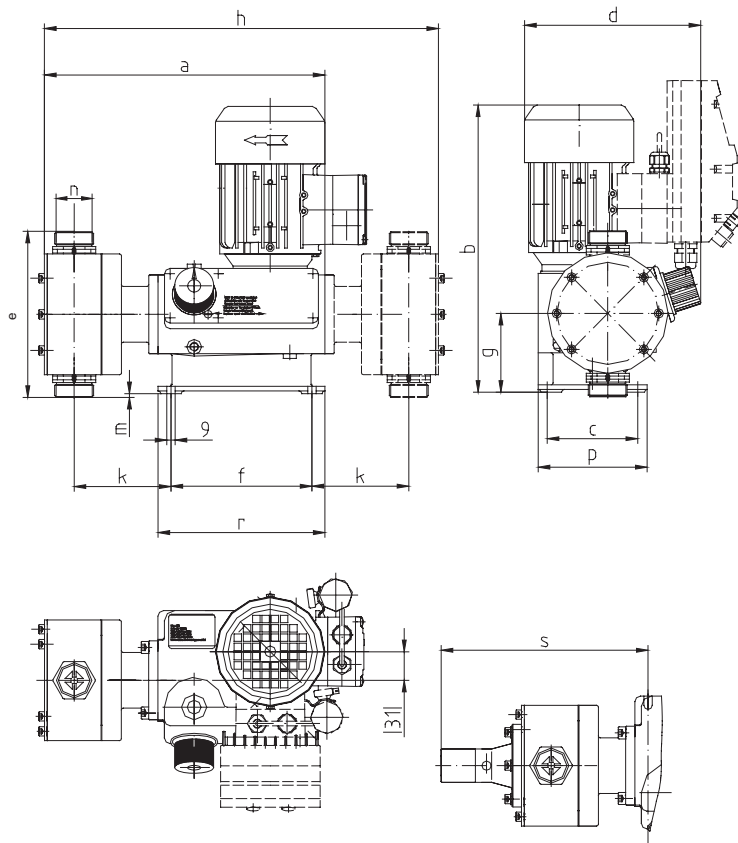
Габаритный чертёж DMX 226 (часть 1)
